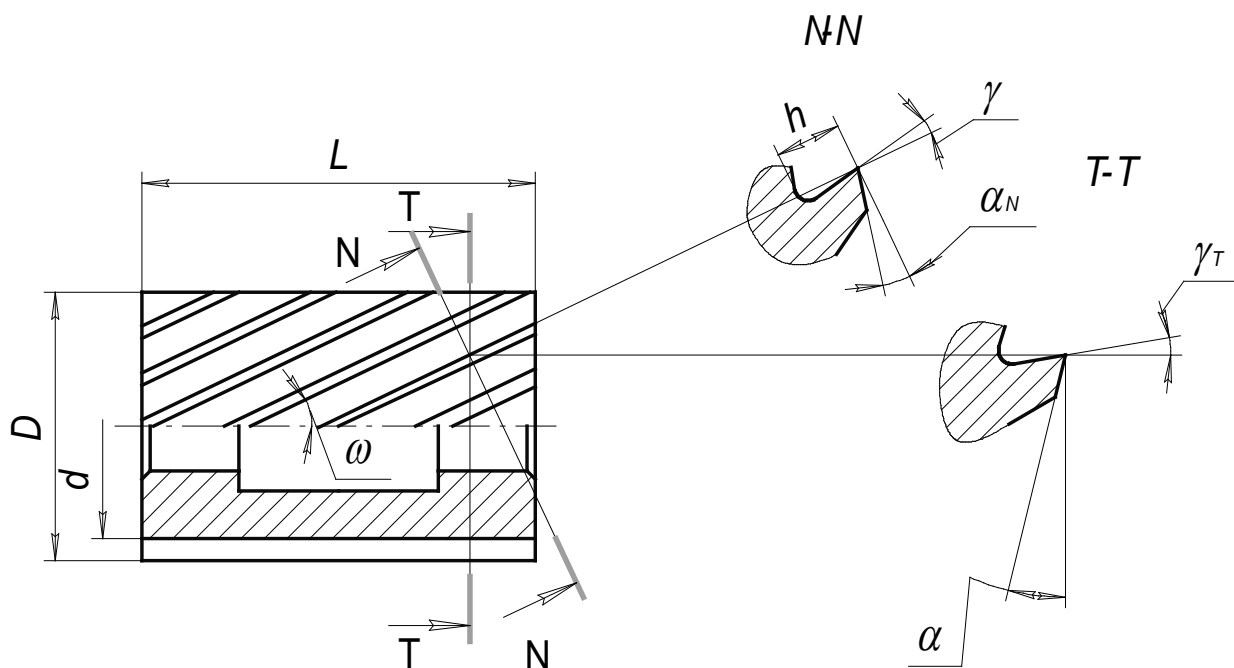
Циліндрична фреза з гвинтовим зубом
